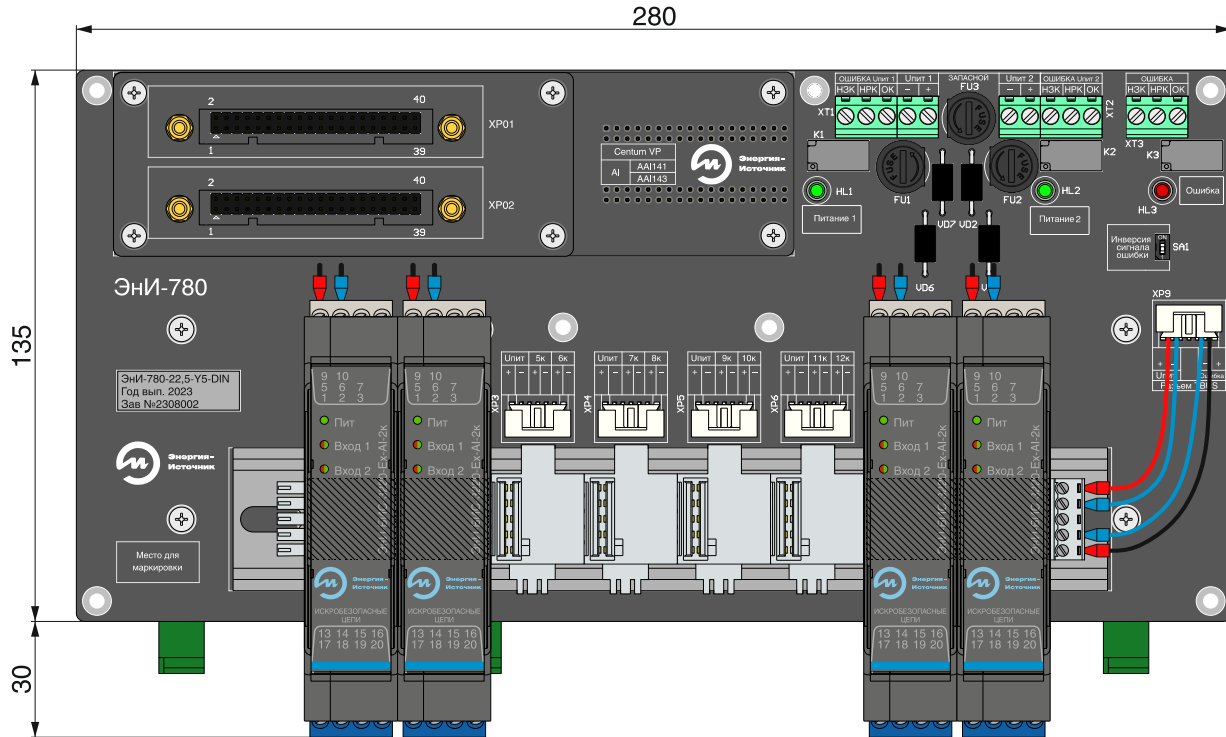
Габаритные размеры платы для восьми приборов с корпусом шириной 22,5 мм
